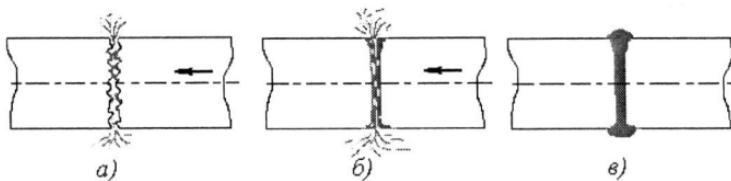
Стыковая сварка оплавлением
